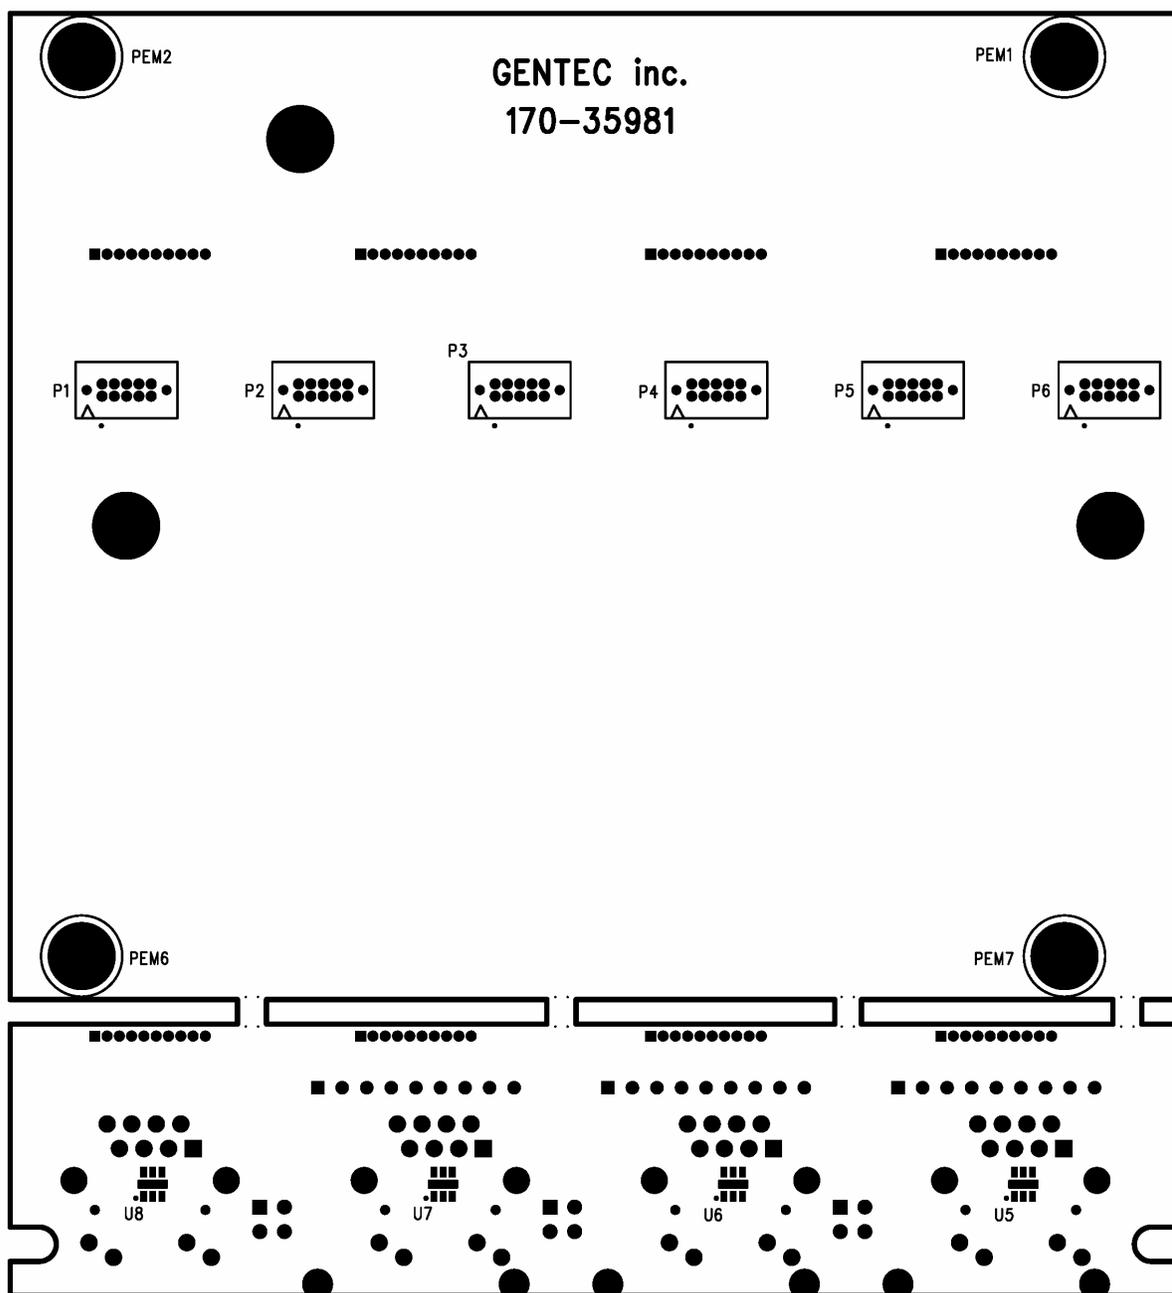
Schéma d'encombrement de la CCE3 (vue de dessous)
